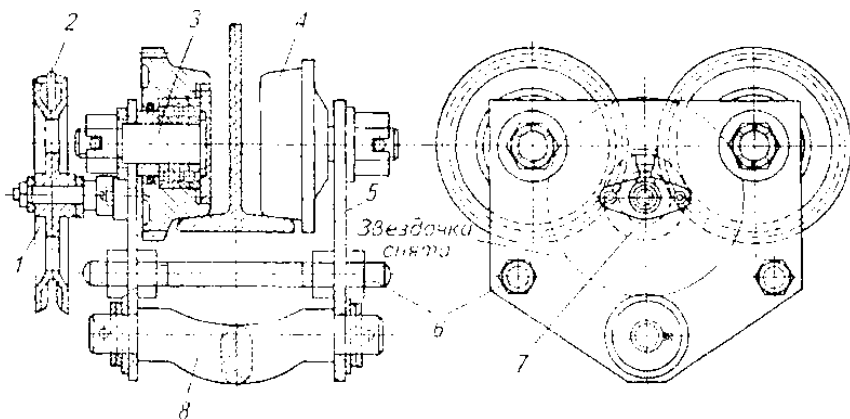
Тележка с ручным механизмом передвижения: 1 – тяговое колесо; 2 – тяговая цепь; 3 – ось ходового колеса; 4 – ходовое колесо; 5 – рама; 6 – стяжка; 7 – передаточный механизм; 8 – траверса
